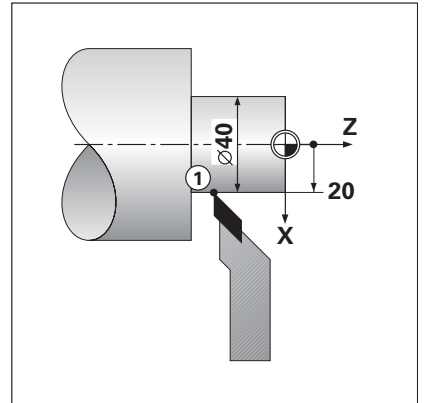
Werkstück zum Beispiel „Durchmesser- und Radius-Anzeige“
